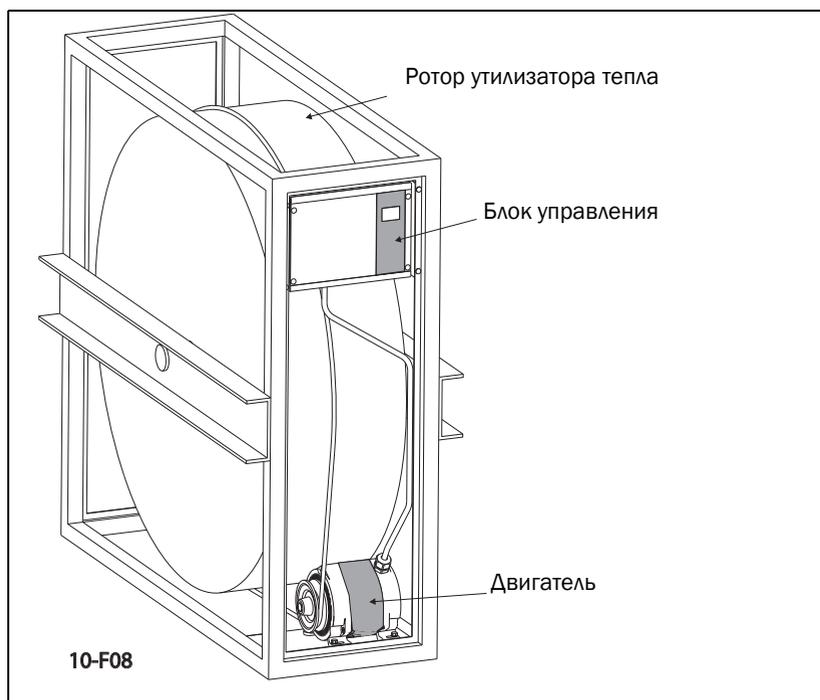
Двигатель и контроллер Emotron роторного утилизатора тепла
